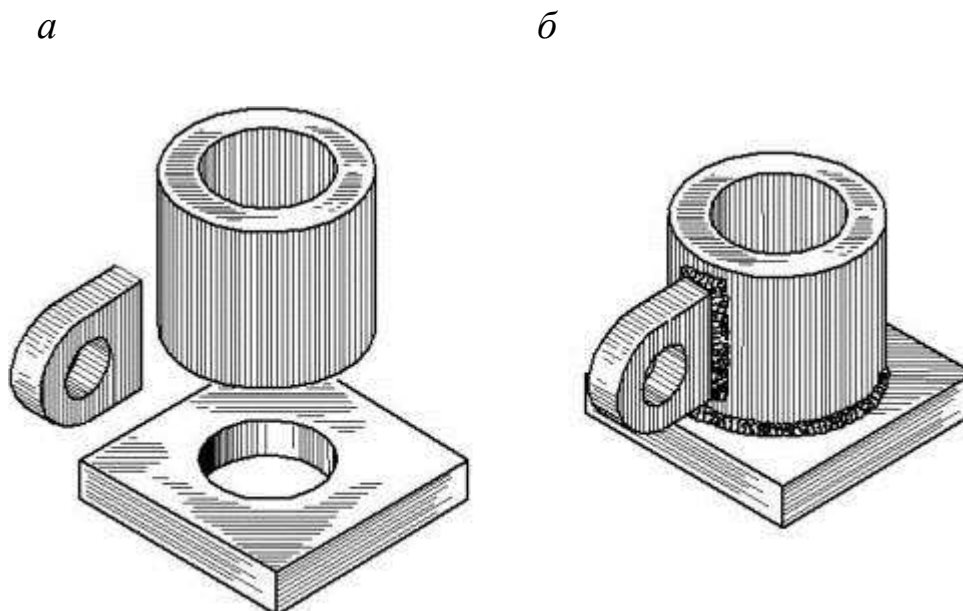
Детали, подготовленные для сварки (*а*),
